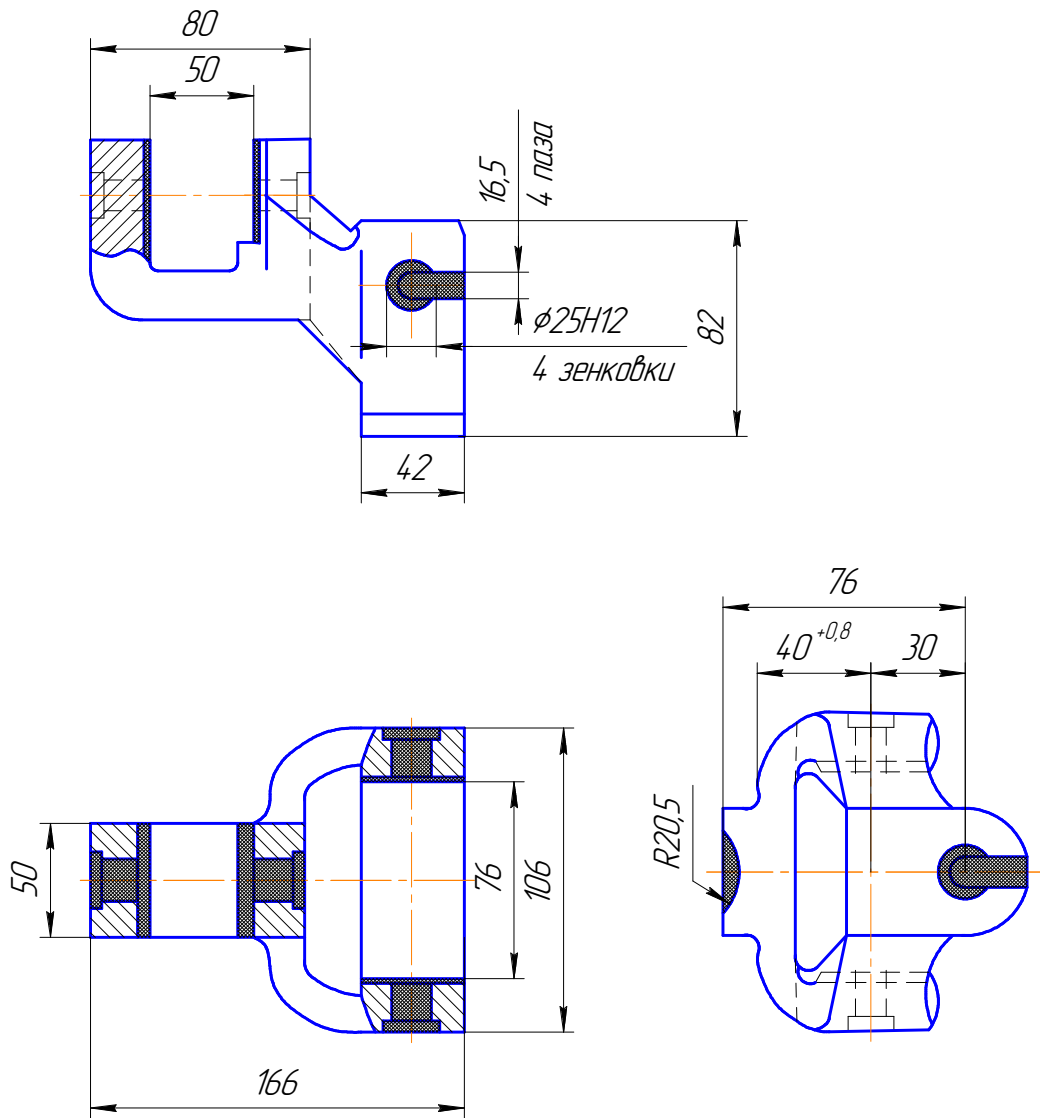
Заготовка кронштейну з призначеними припусками і допусками
